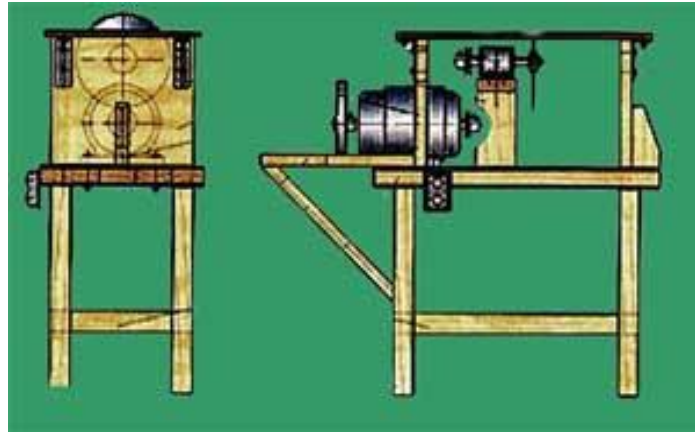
Саморобний верстат з дерев'яною несучою системою[3].
